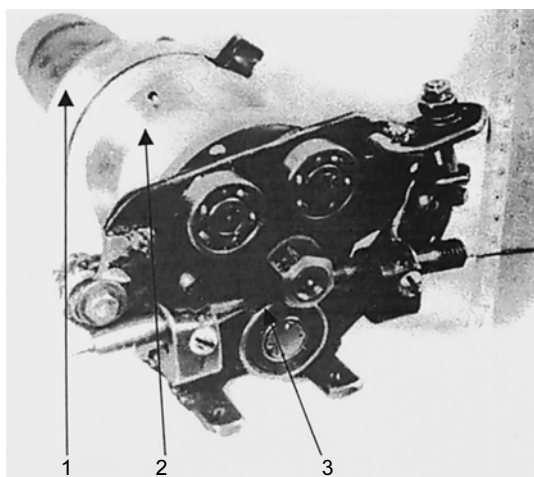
Вариант конструкции механизма импульсной подачи с КВП: 1 — приводной электродвигатель; 2 — КВП; 3 — устройство прижима с разгрузкой выходного вала
